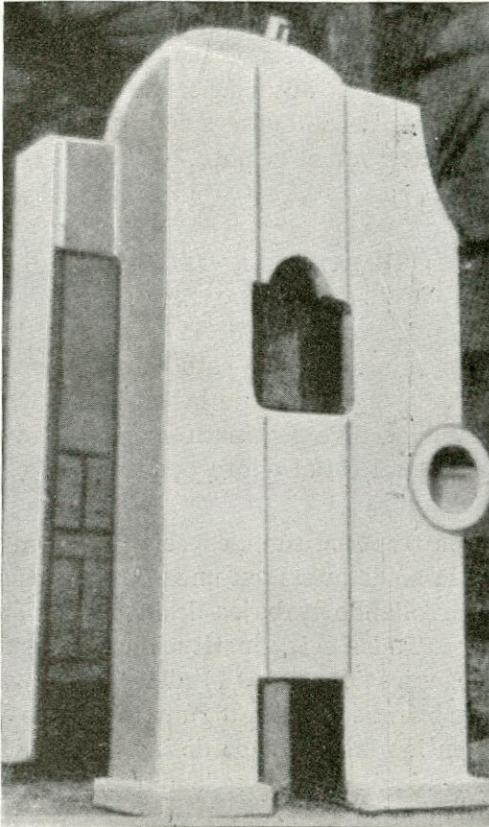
Estructura de una prensa de forja de 4.000 ton. fabricada por soldadura eléctrica "Electro-slag".
